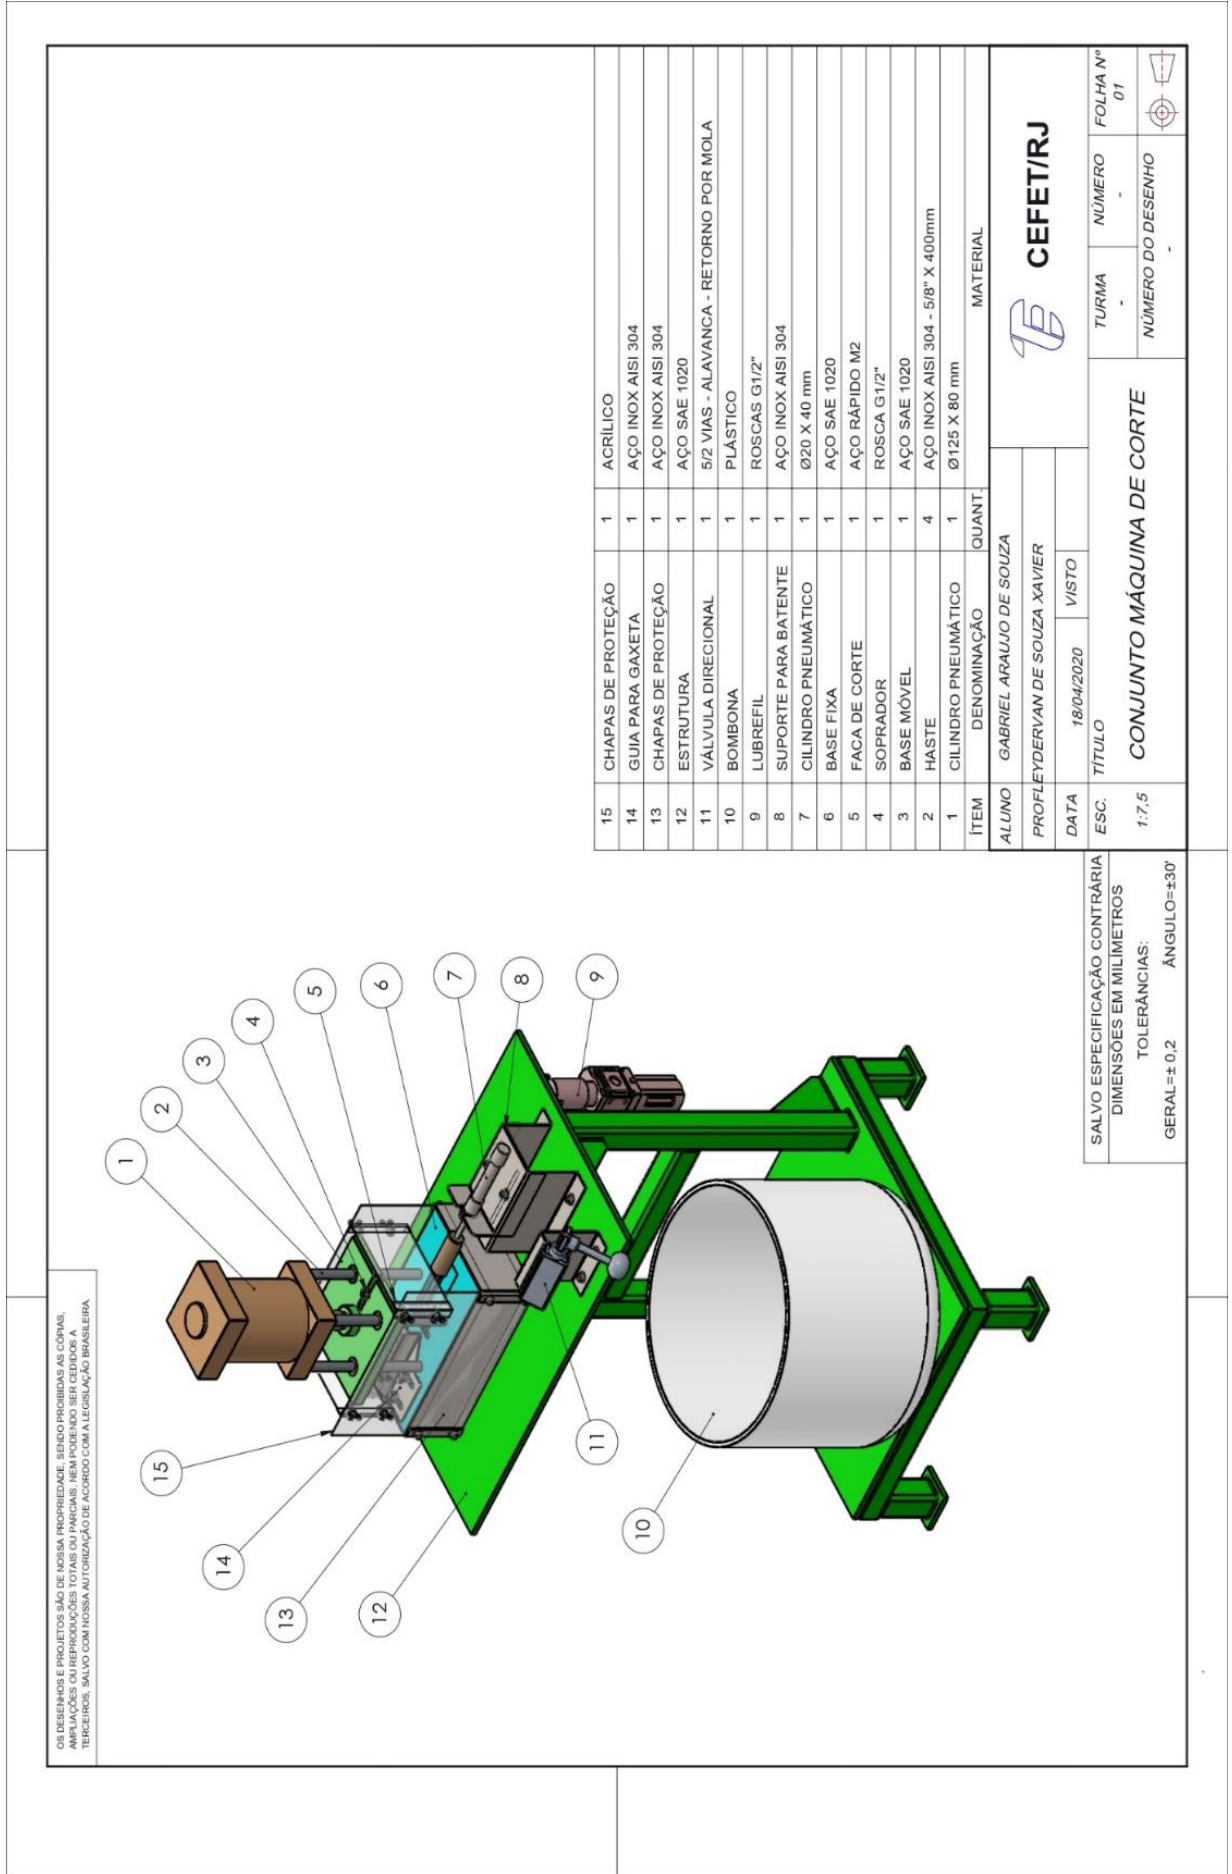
Desenho de conjunto da máquina com principais elementos [Autoria própria].
